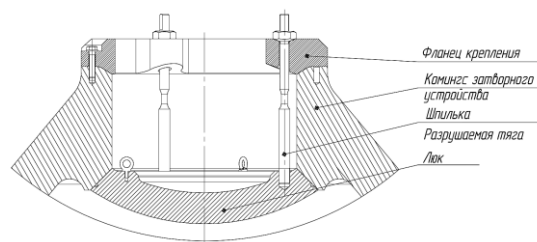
Принципиальный чертеж устройства аварийного сброса давления
